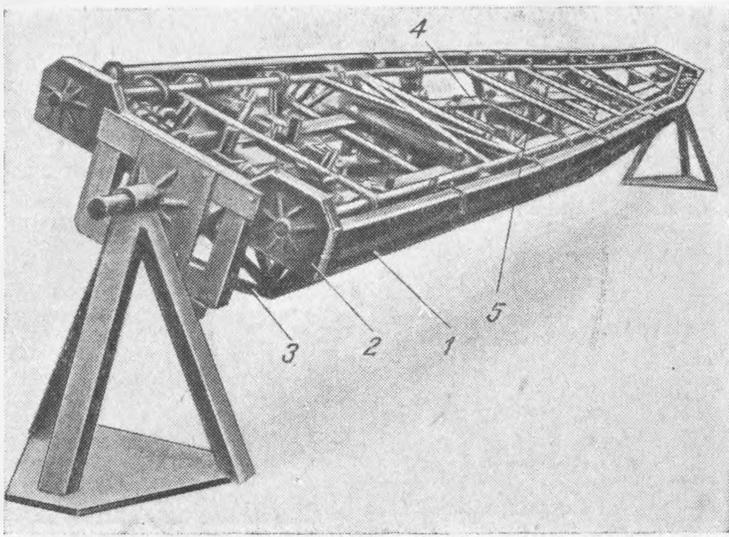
Стапель для сборки и сварки моторама.
